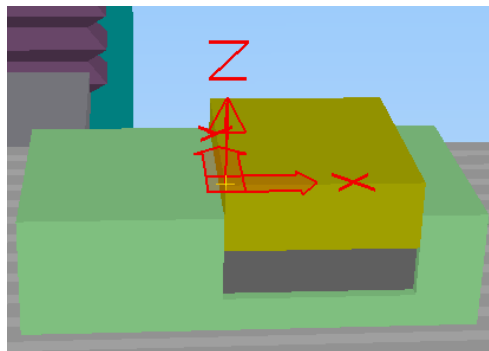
Осі координат встановленої нульової точки заготовки
